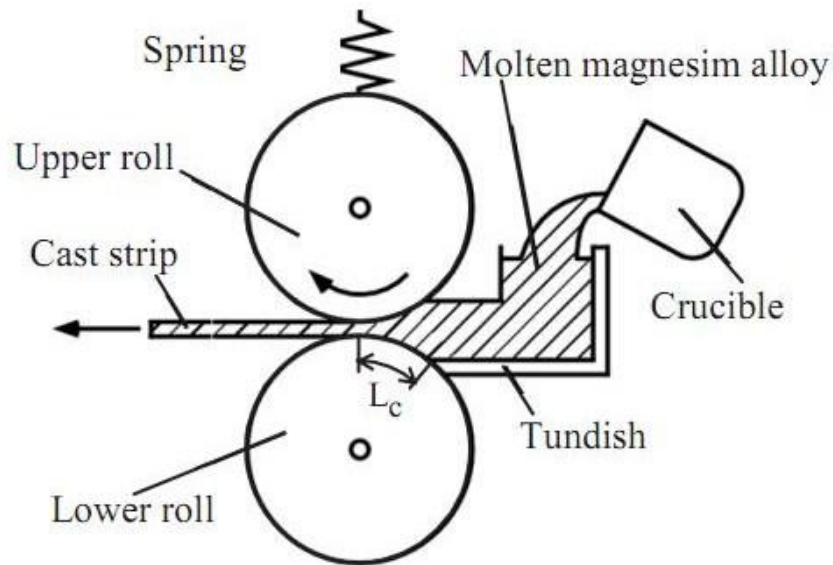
Schema illustrativo di un Twin-Roll casting orizzontale
